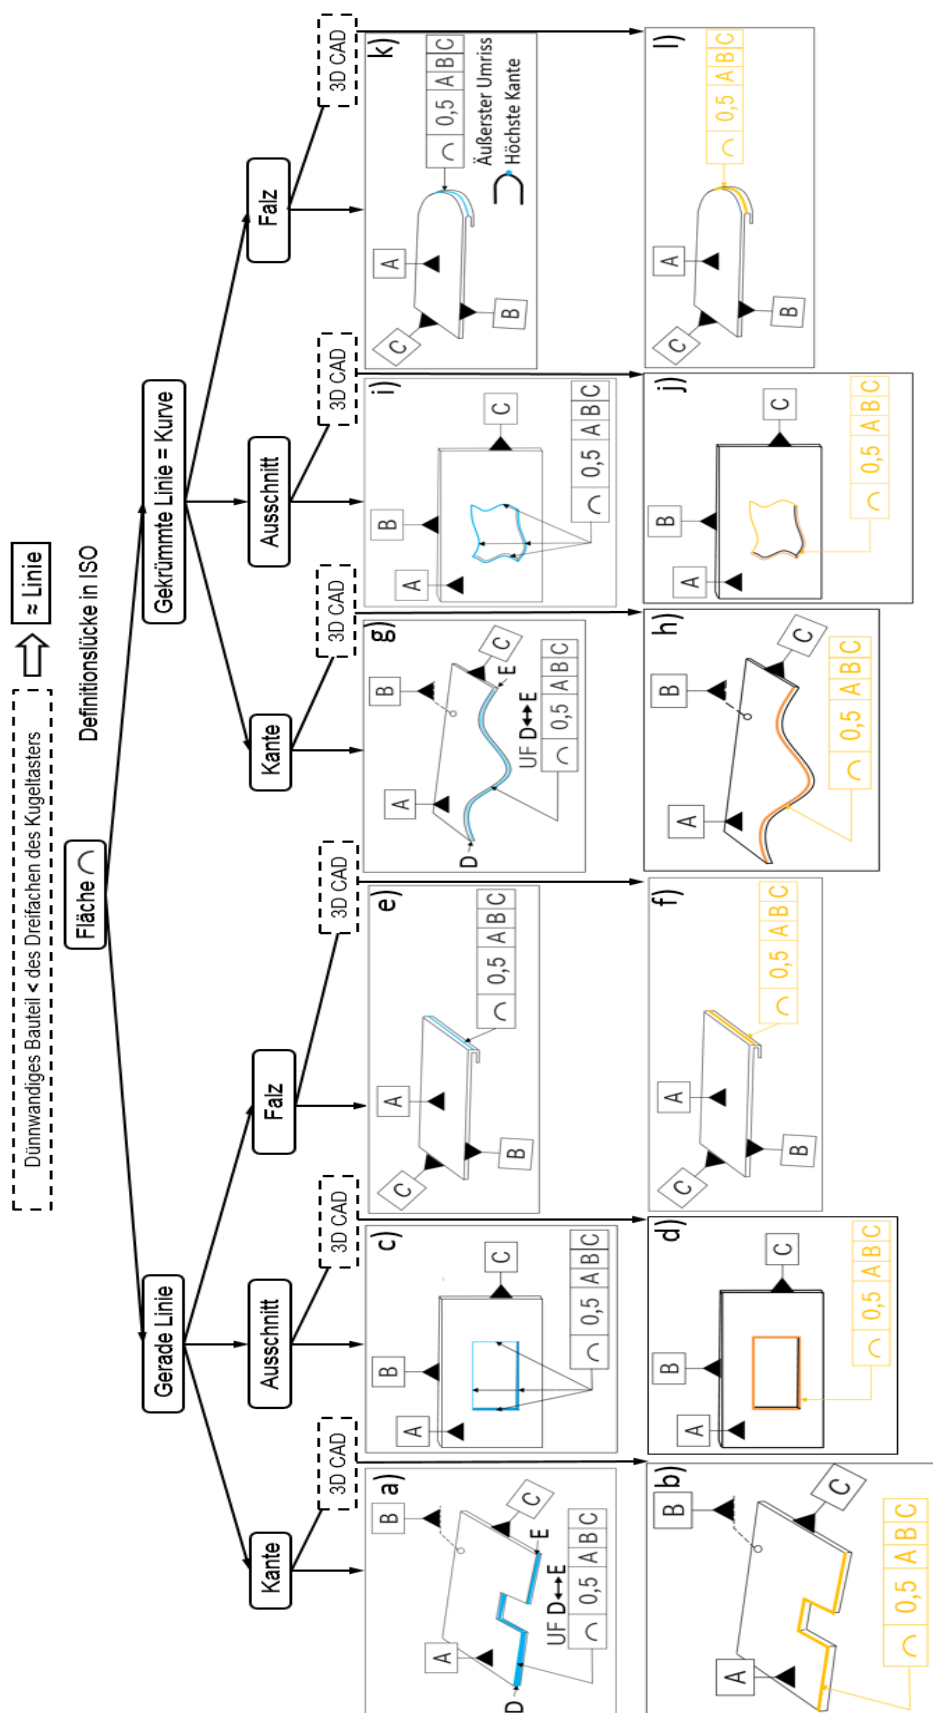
Gesamte Systematik für die Tolerierung einer realen, sehr dünnen Fläche mit Linienprofilltoleranz
